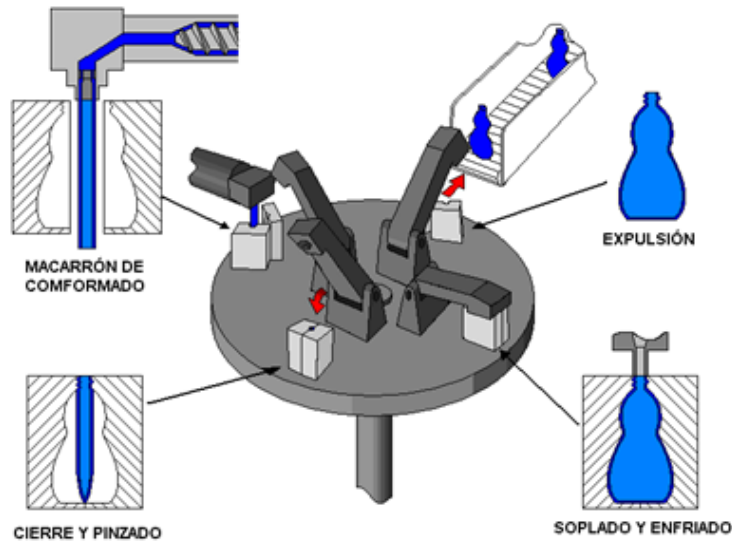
Máquina de extrusión-soplado tipo rotatorio
